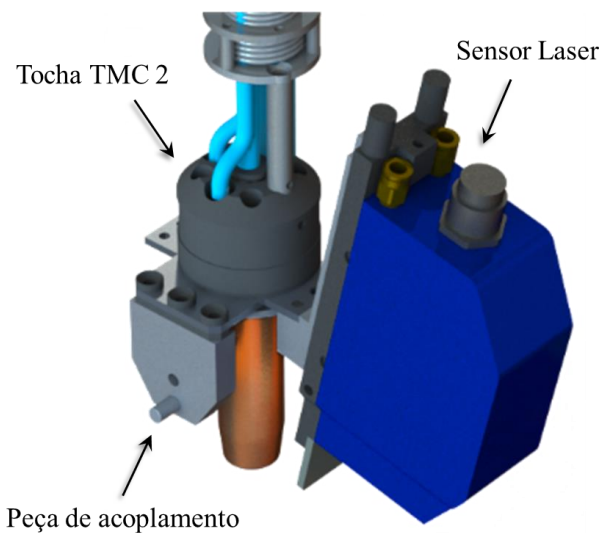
Representação em CAD da peça de acoplamento montada ao conjunto Tocha/Laser.
